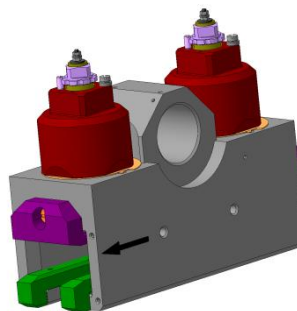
Общий вид тормозного башмака с установленными ПАДами
